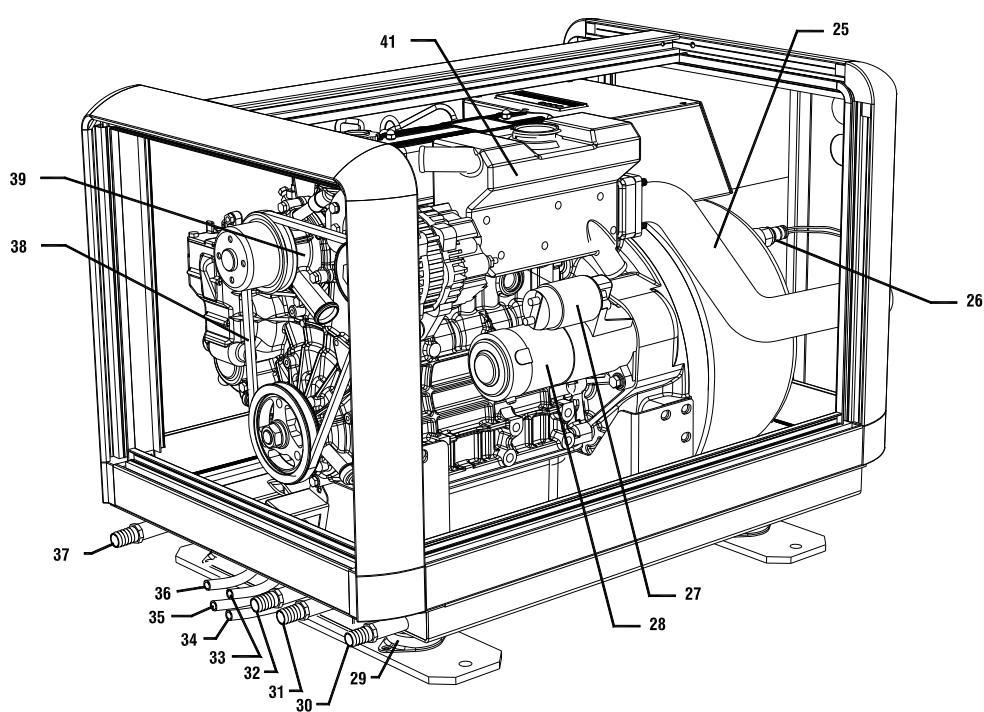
Vue arrière des composants principaux du Whisper 6 et 10
